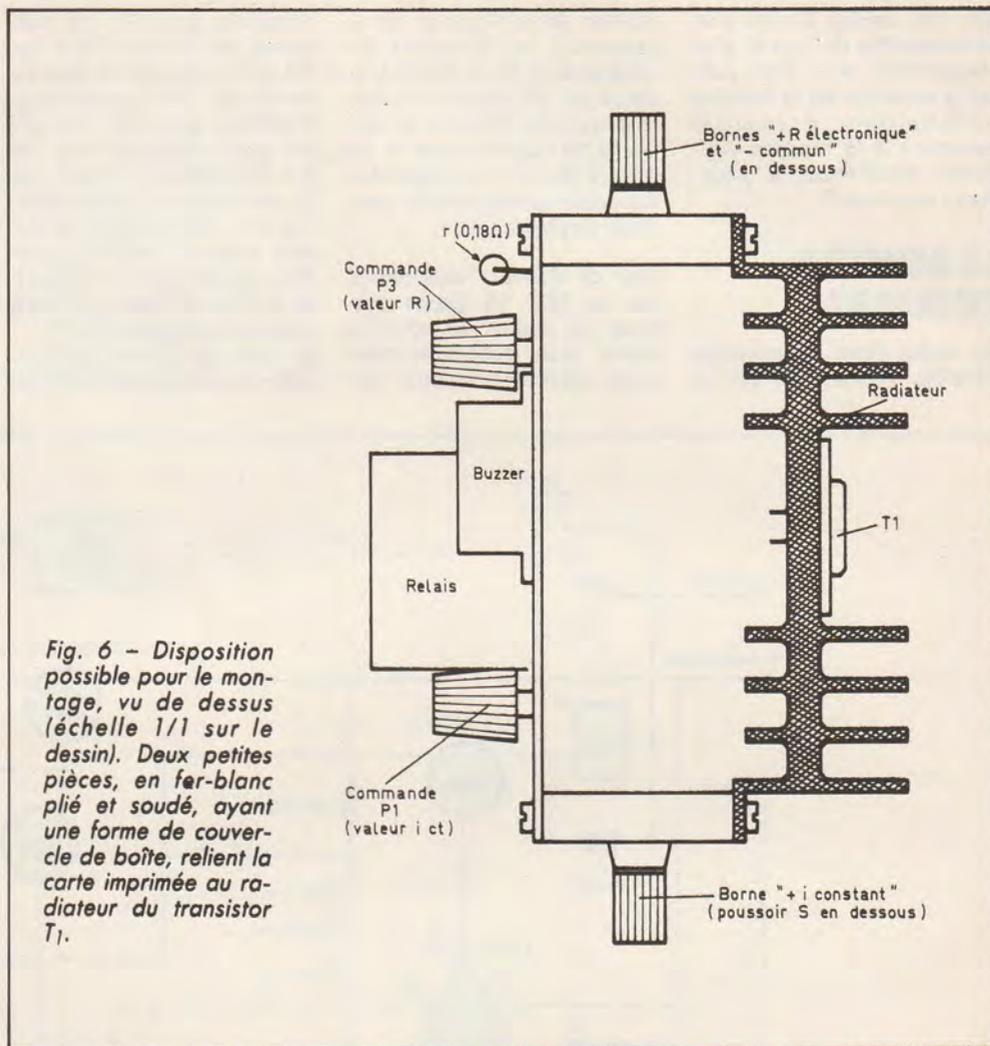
Disposition possible pour le montage, vu de dessus (échelle 1/1 sur le dessin). Deux petites pièces, en fer-blanc plié et soudé, ayant une forme de couvercle de boîte, relient la carte imprimée au radiateur du transistor T_1 .
